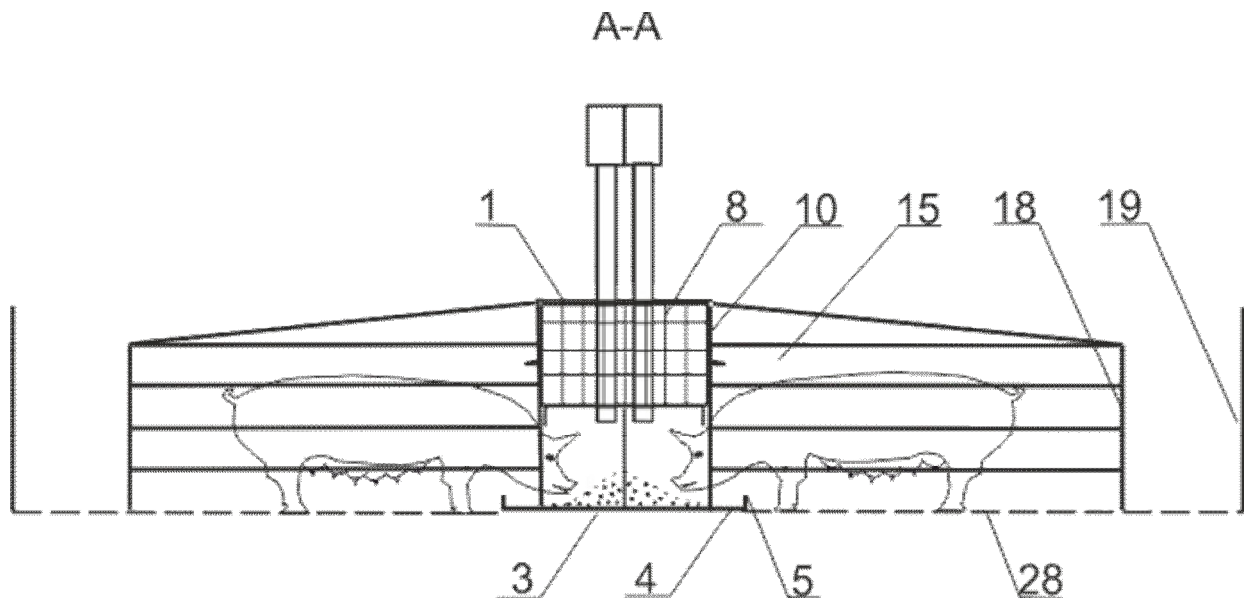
Вигляд збоку станка, розріз А-А на рис. 3.6
